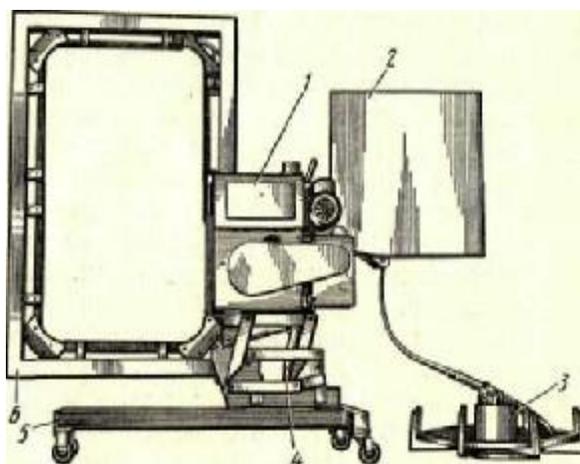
Машинка для обвязки металлическими лентами из бухты:
